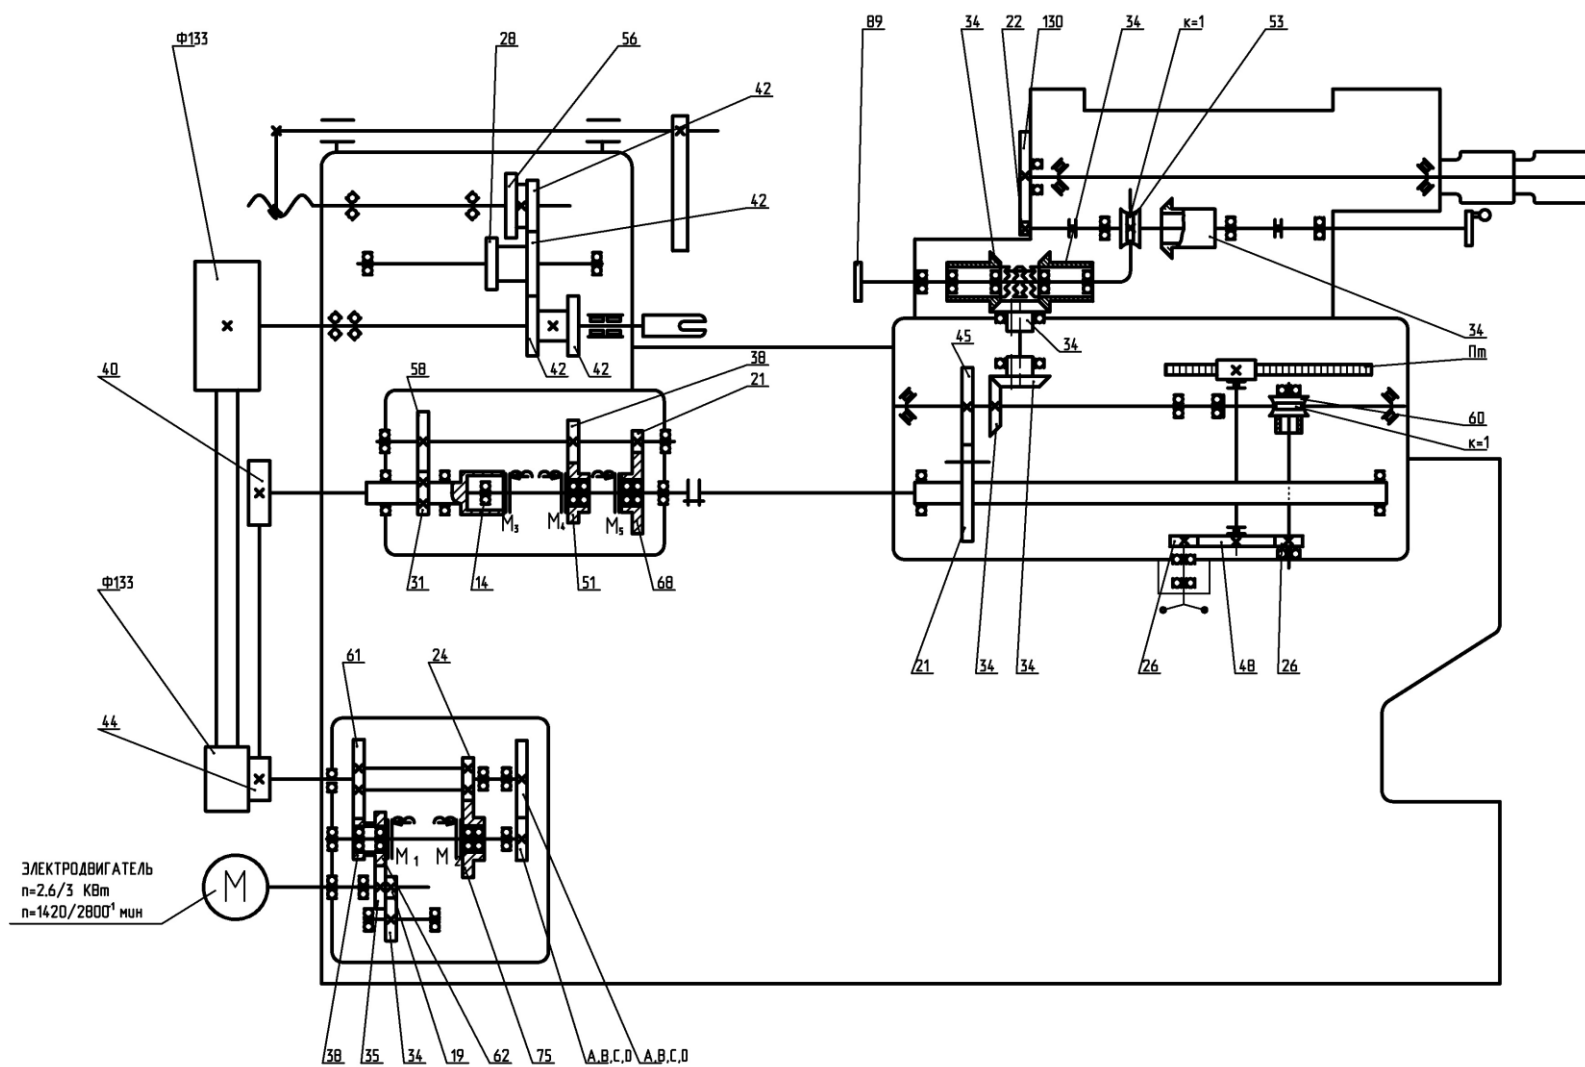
Кинематическая схема токарно-револьверного станка модели 1Г325
